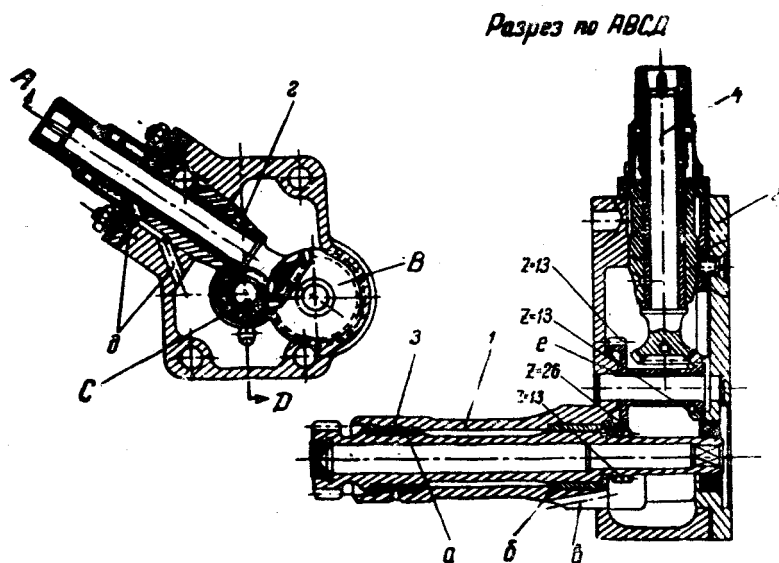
Привод топливного насоса и генератора тахометра: 1—корпус привода; 2—крышка корпуса; 3—валик привода бензонасоса; 4—валик привода генератора тахометра
